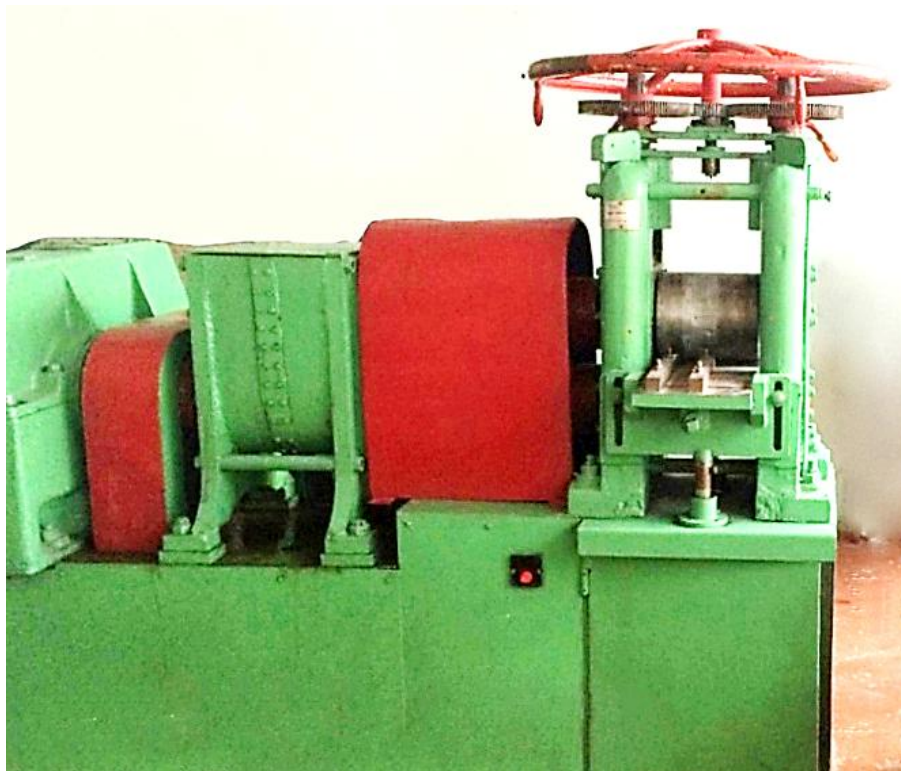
Лабораторний двовалковий прокатний стан 180
